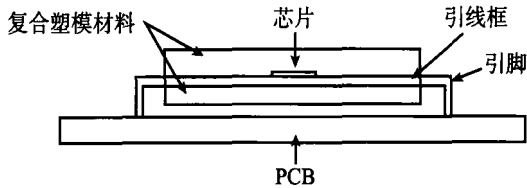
塑料 DIP 焊接在 PCB 上的截面结构
